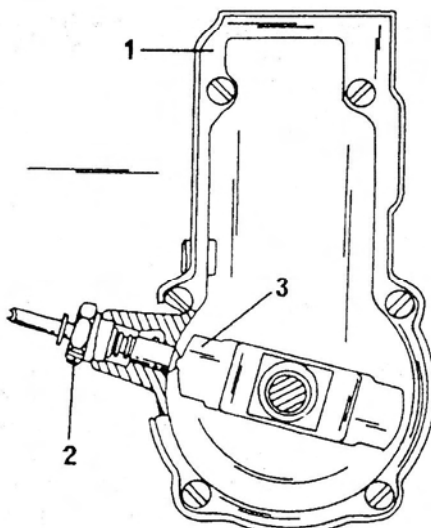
Блокировка регулятора внутри топливного насоса высокого давления стопорным винтом.
